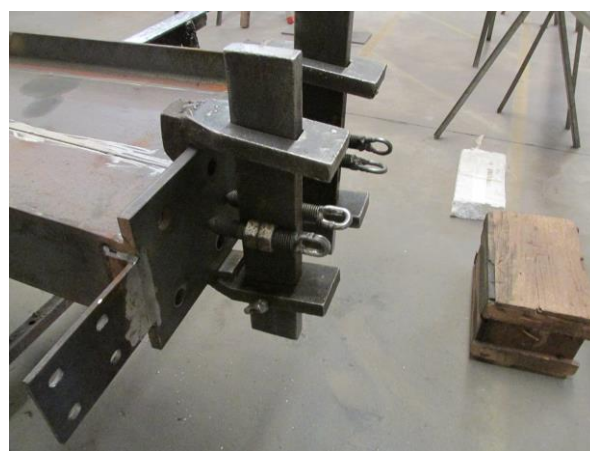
Dispositivo rígido para auxiliar na soldadura de chapa de topo de asna
